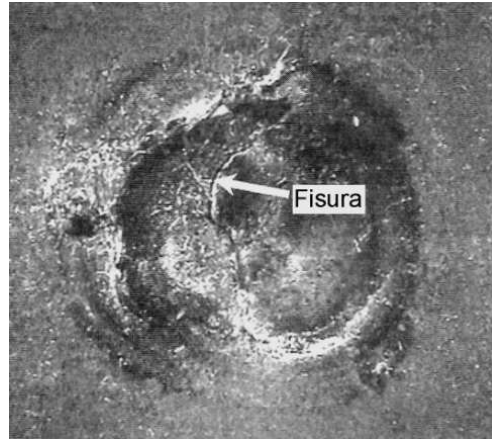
20. Fisura en la superficie de soldadura.<sup>24</sup>
